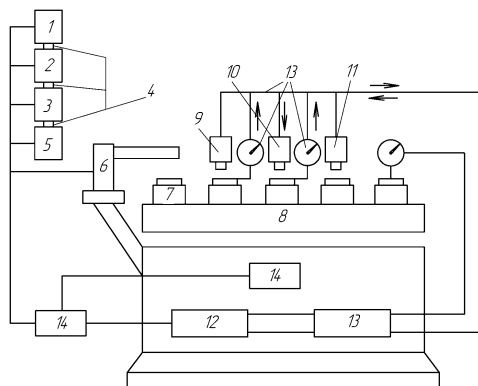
Схема автоматического сборочного станка: 1, 2, 3, 4, 5 – загрузочное устройство и его функциональные узлы (бункер, механизм ориентации, накопитель и т.п.); 6 – комбинированный питатель; 7 – приспособление; 8 – транспортное устройство; 9, 10, 11 – рабочие головки, осуществляющие процесс сборки, обработку в процессе сборки, нанесение покрытий и т.п.; 12 – командоаппарат; 13 – контрольные устройства; 14 – силовые системы.
